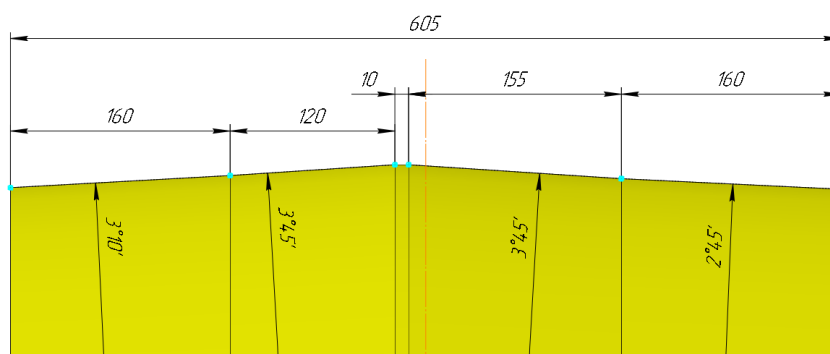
Калибровка валка прошивного стана ТПА 220 в текущей технологии
